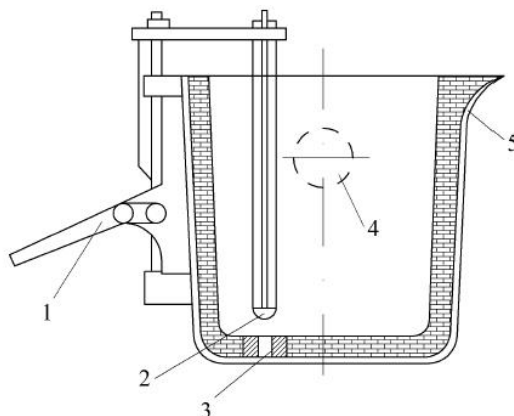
Общий вид двухстопорного сталеразливочного ковша:
